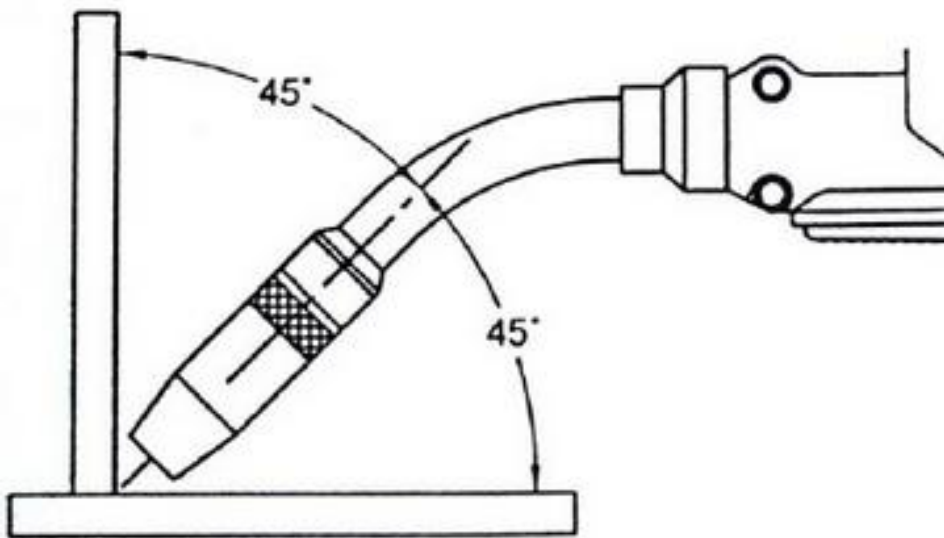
Efecto de la posición del electrodo y de la técnica de soldadura.
